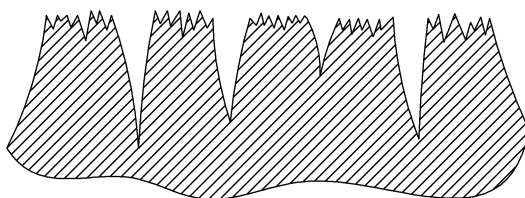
Профиль поверхности цилиндра при плосковершинном хонинговании
